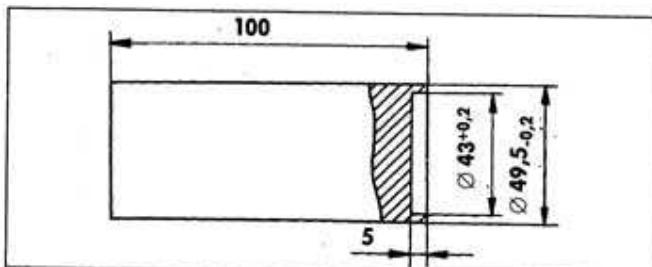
Оправка для выпрессовки резинометаллического шарнира из ушек рессор. Материал – сталь 40X (HRC 30–34)
